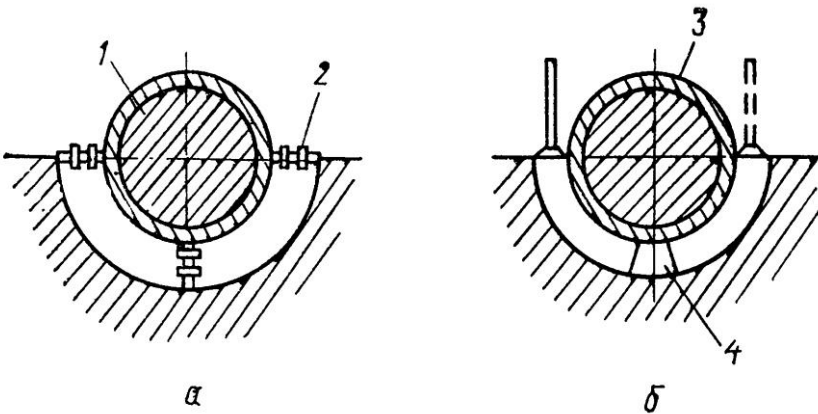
Вимірювання під час центрування ротора за розточками:
